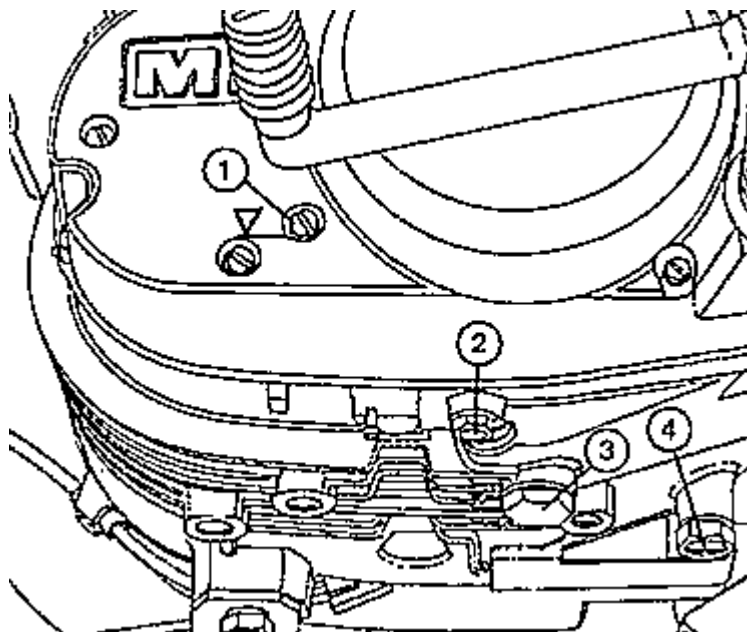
Ölkontrollschraube und Ölablaßschrauben
